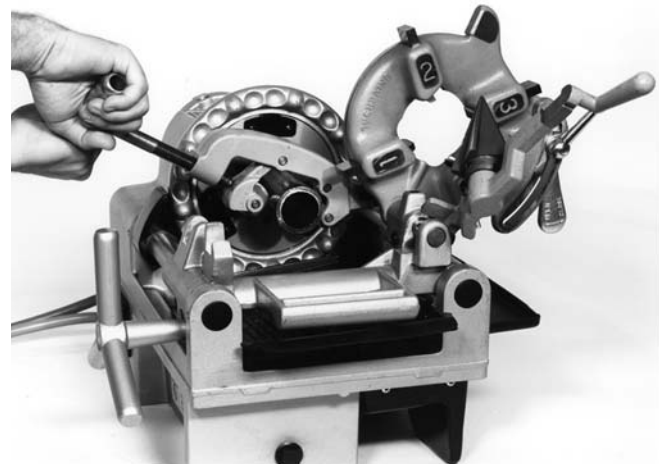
Coupe des tuyaux à l'aide du coupe-tubes n° 732
